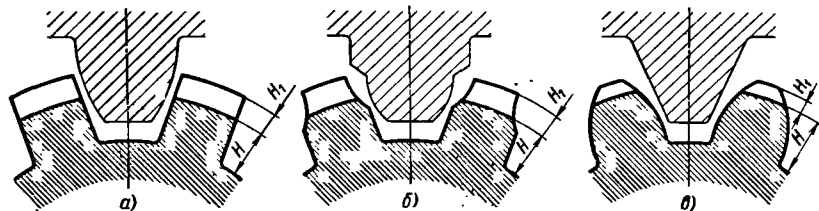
Обработка шлицев с прорезными упорными буртиками:
